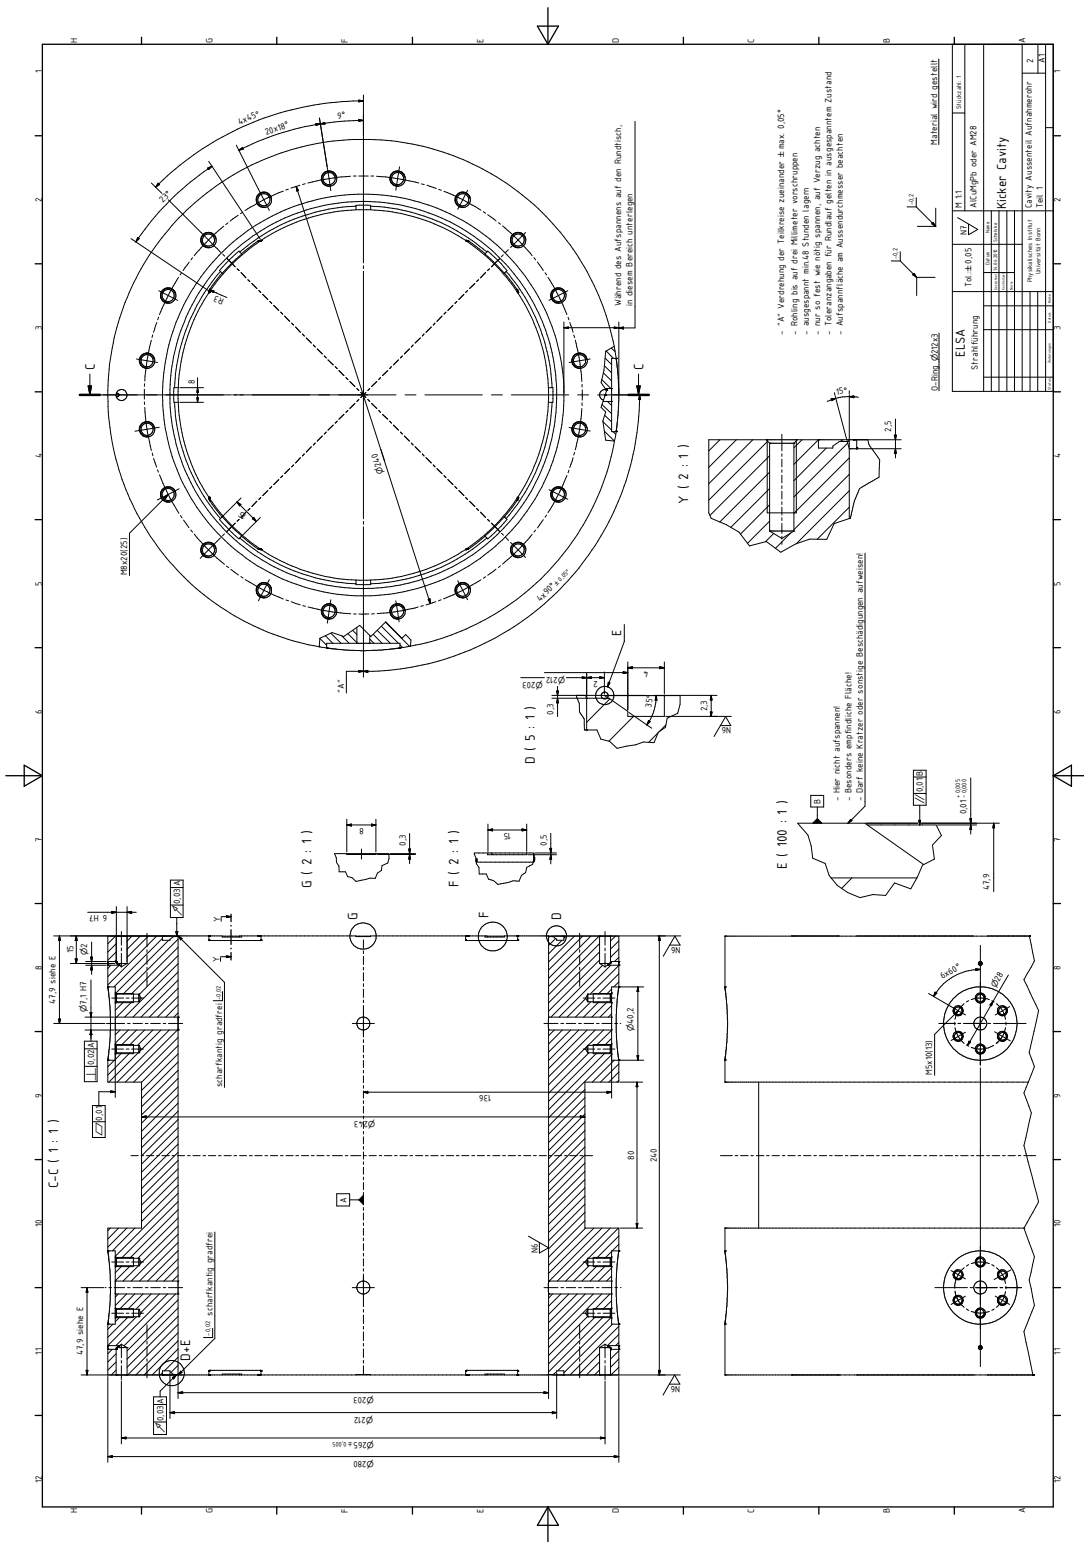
Technische Zeichnung des Kicker-Cavities, erster Teil.
